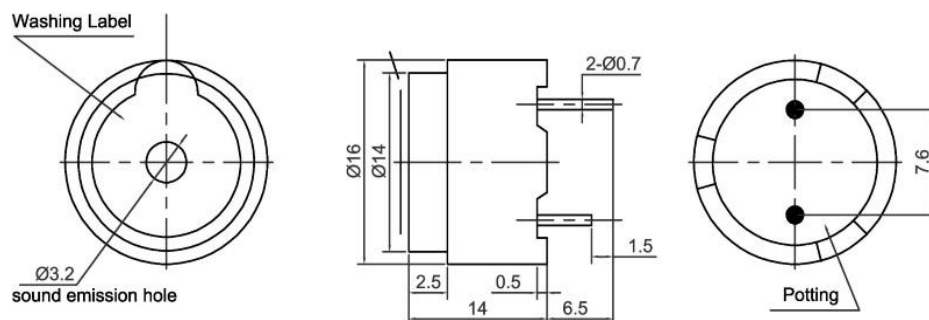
Зовнішній вигляд зумера HCM1606X
